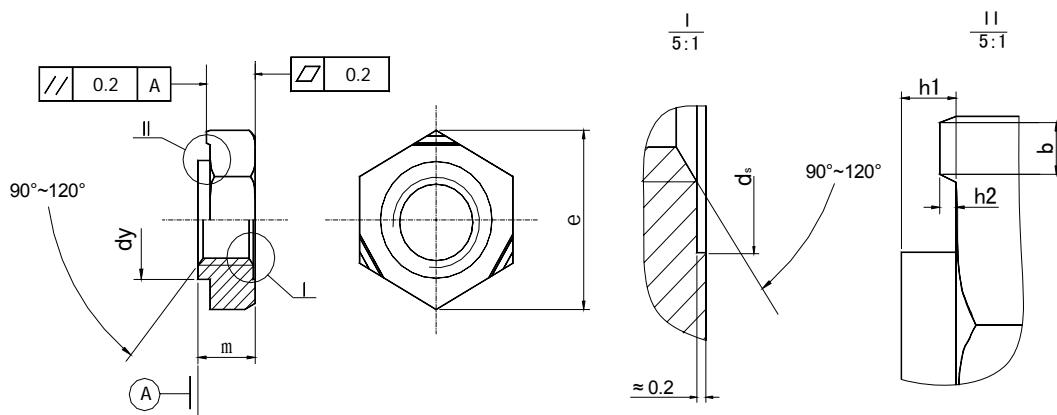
焊接六角螺母 GB13681-92 结构型式
